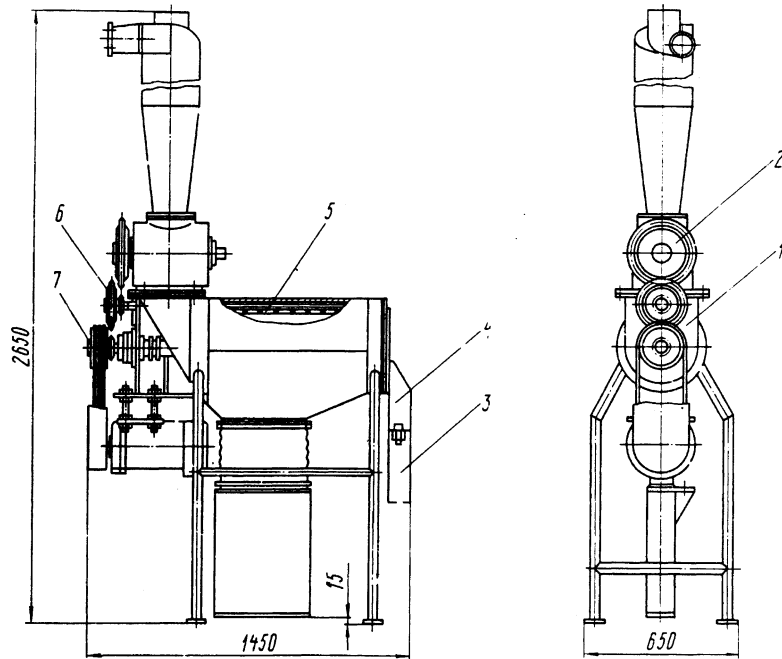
Загальний вигляд просіювача борошна Ш2-ХМВ:
